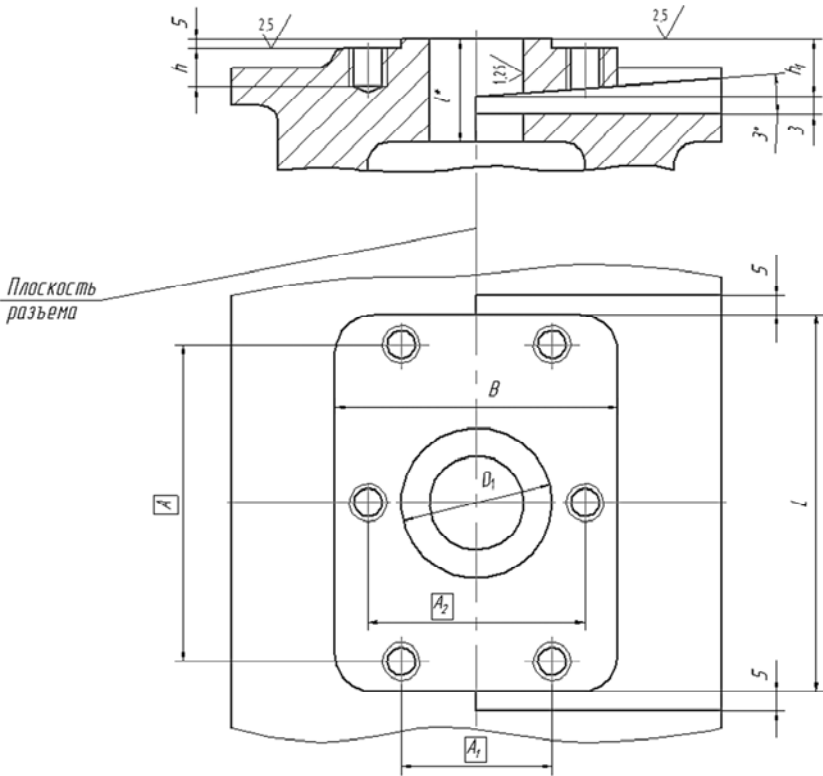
Конструкция платика для установки гидравлического приспособления.
